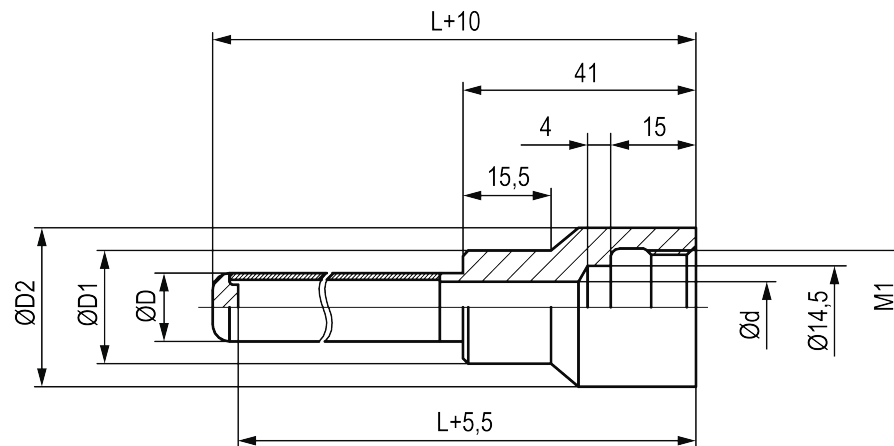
ГЗ.16, ГЗ.25 с присоединением к процессу сваркой (для датчиков с неподвижным штуцером)
